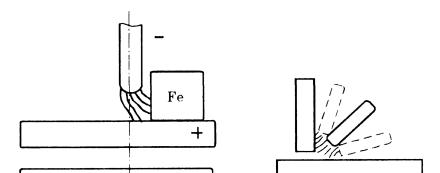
Влияние ферромагнитных масс на сварочную дугу
